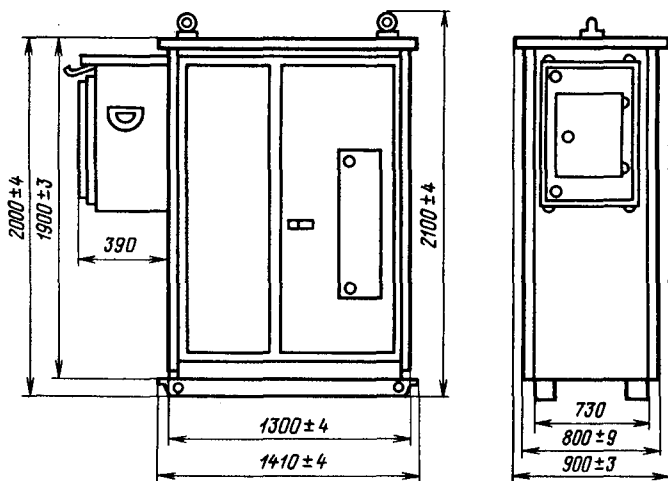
Общий вид габаритные и установочные размеры устройства «Купна»
